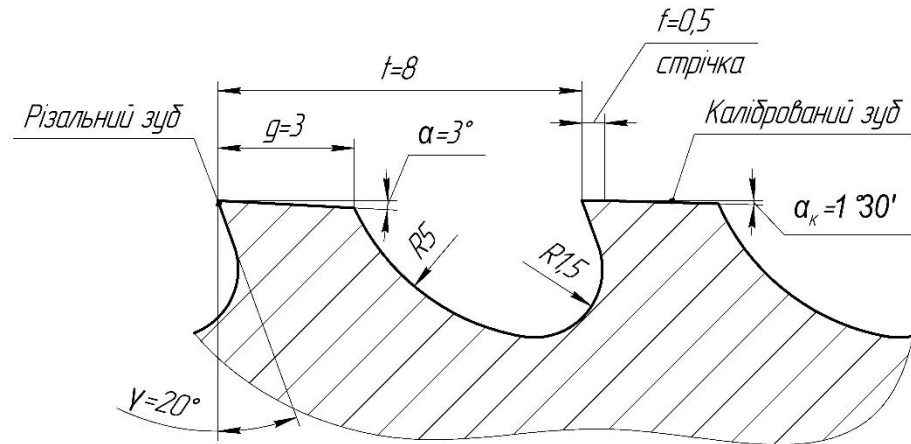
Стружкова канавка різального та каліброваного зубів протяжки
